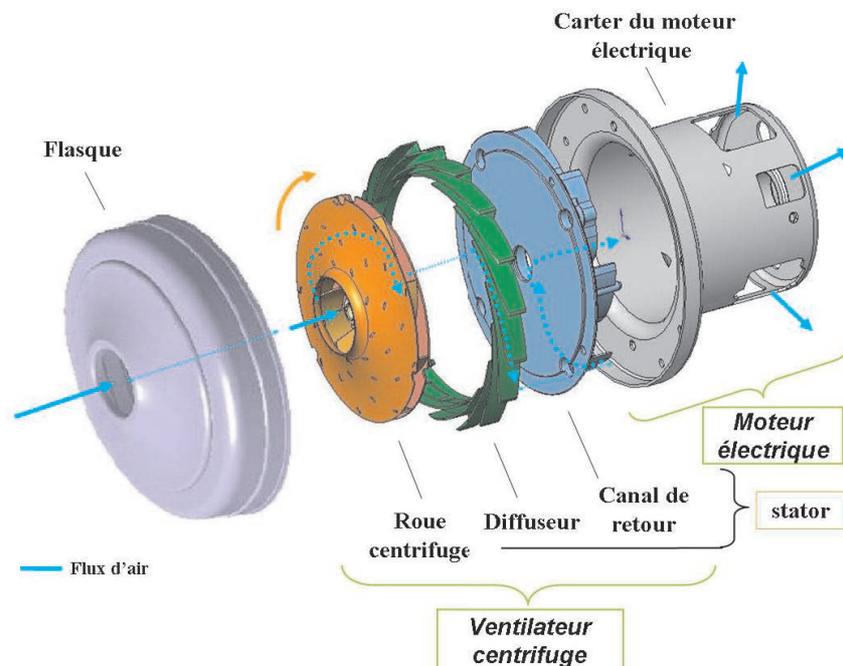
Vue éclatée de la géométrie du moto-ventilateur étudié.
